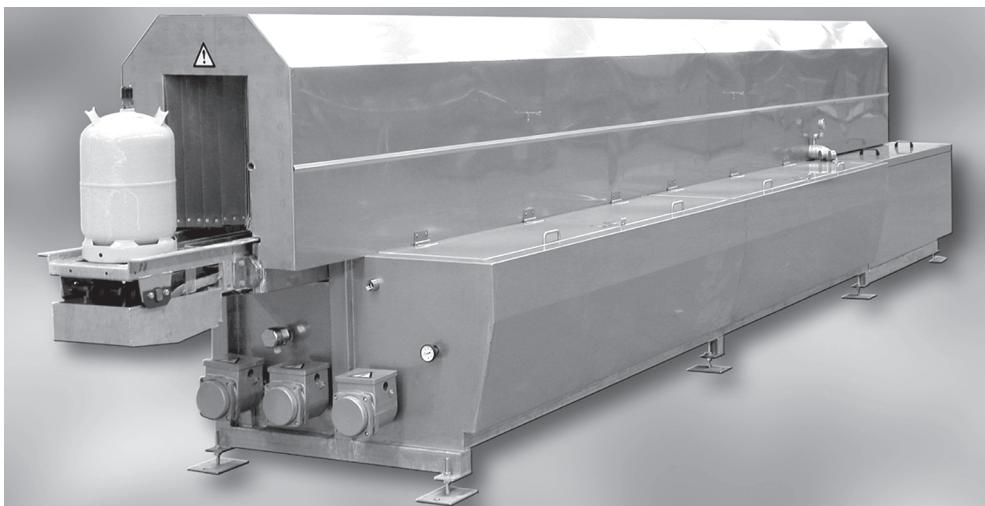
Резервуар для воды WT-2500, встроенный в карусель для проверки давлением
